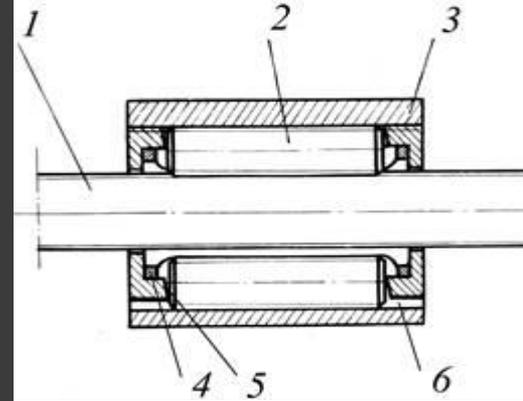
Передача с короткими резьбовыми роликами с рециркуляцией роликов: 1 – винт; 2 – резьбовые ролики; 3 – гайка; 4 – пространственный сепаратор; 5 – кулачок; 6 – продольный паз в гайке
